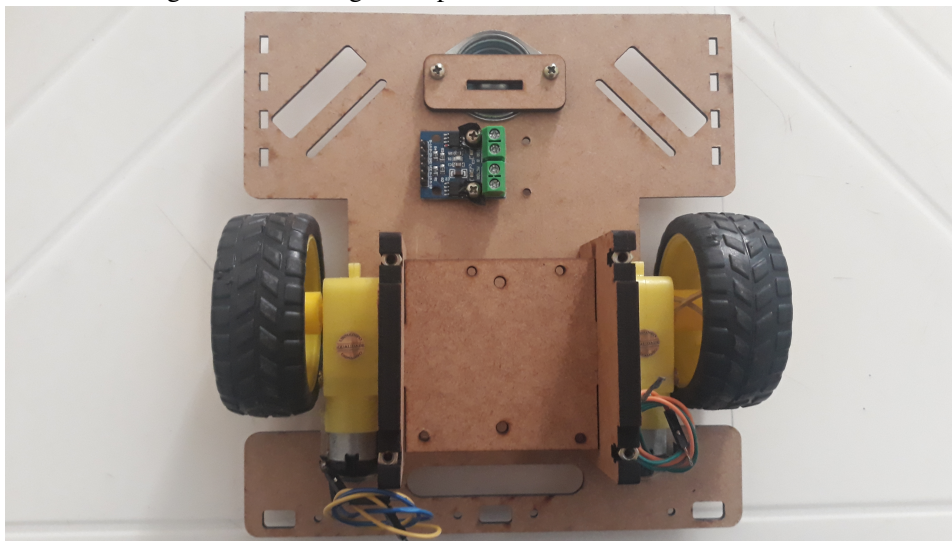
Montagem do segundo conjunto roda motor suporte.
